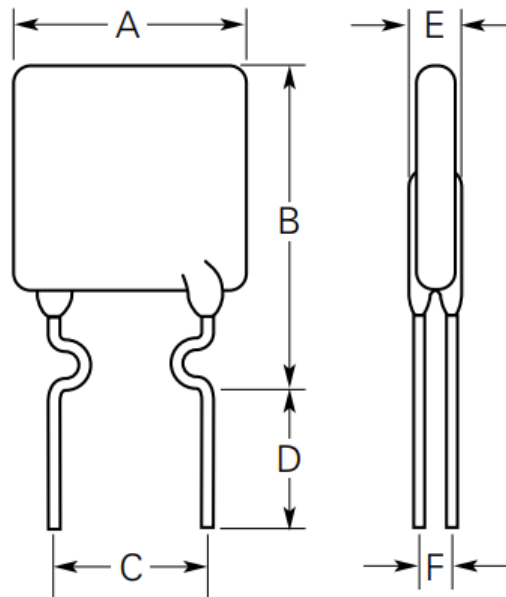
Габаритні розміри резистора RUEF300
